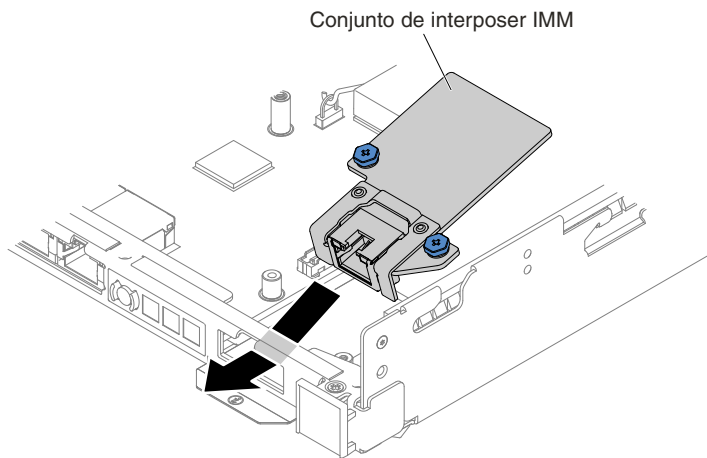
Instalação do conjunto de cabo adaptador de IMM
